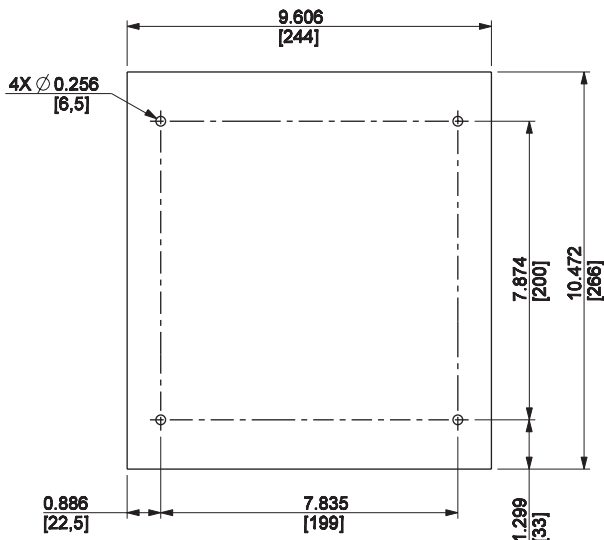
Dimensions des trous de montage et des découpes du couvercle du boîtier
